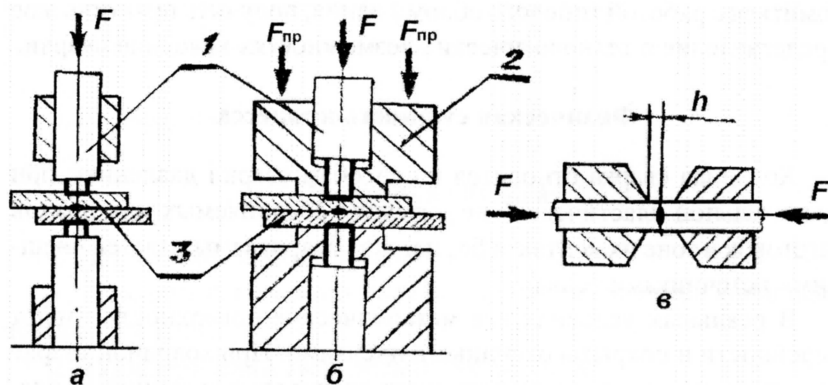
Схема холодной сварки: а – незажатых заготовок; б – предварительно зажатых; в – стержней; 1 – пуансон; 2 – прижим; 3 – заготовки
